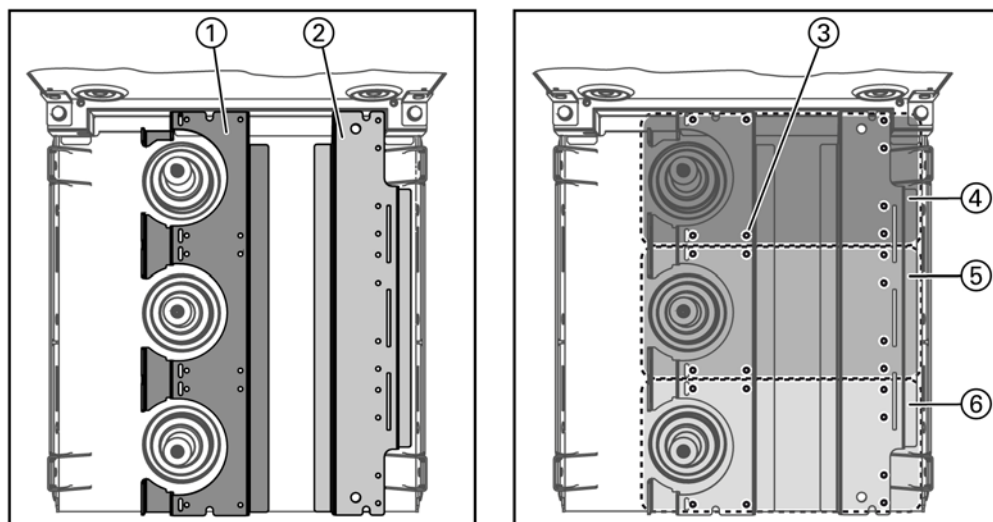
Крепление трансформатора напряжения (вид сверху)
